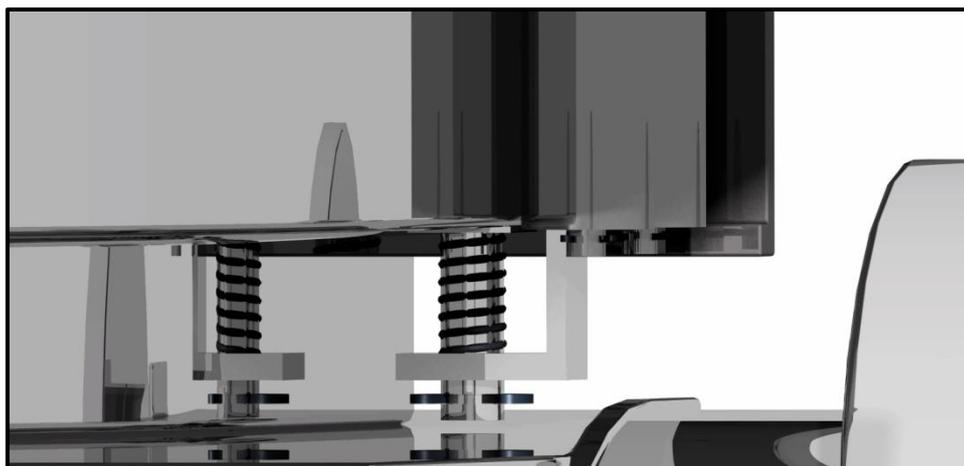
Detalle de la pletina de la palanca en posición de bloqueo.
